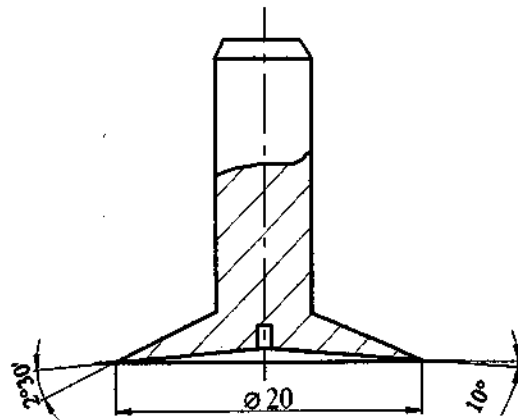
Ножевая фреза для удаления припуска сотового заполнителя
